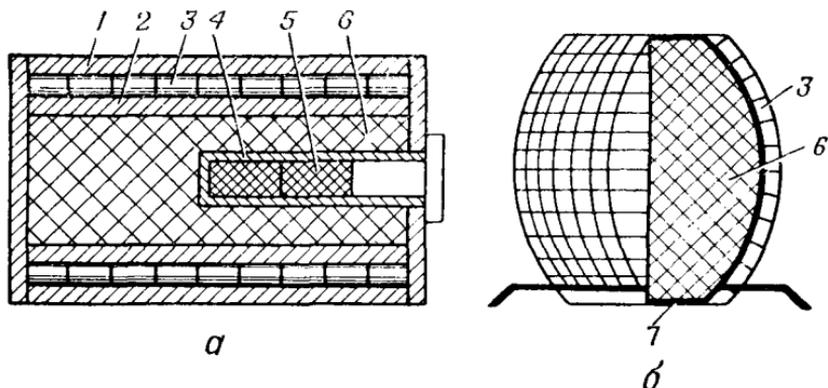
Схемы осколочных боевых частей с готовыми осколками цилиндрической (а) и кубической (б) формы:
